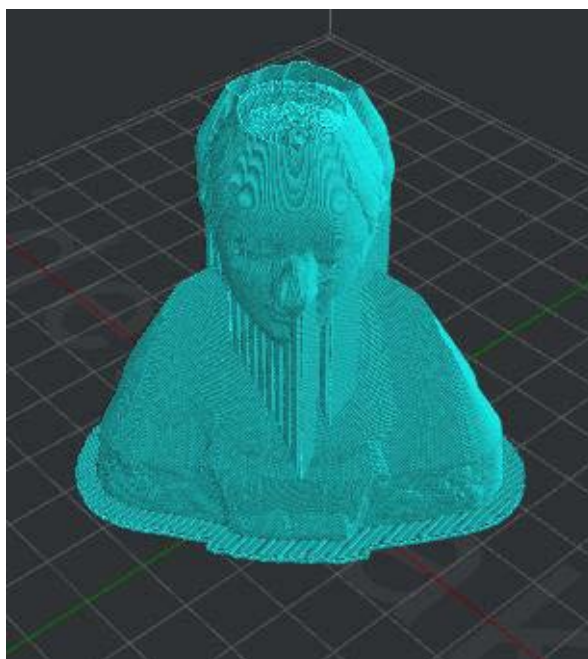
"Wipe Wall Loop Lines" nastavená na dvě.
